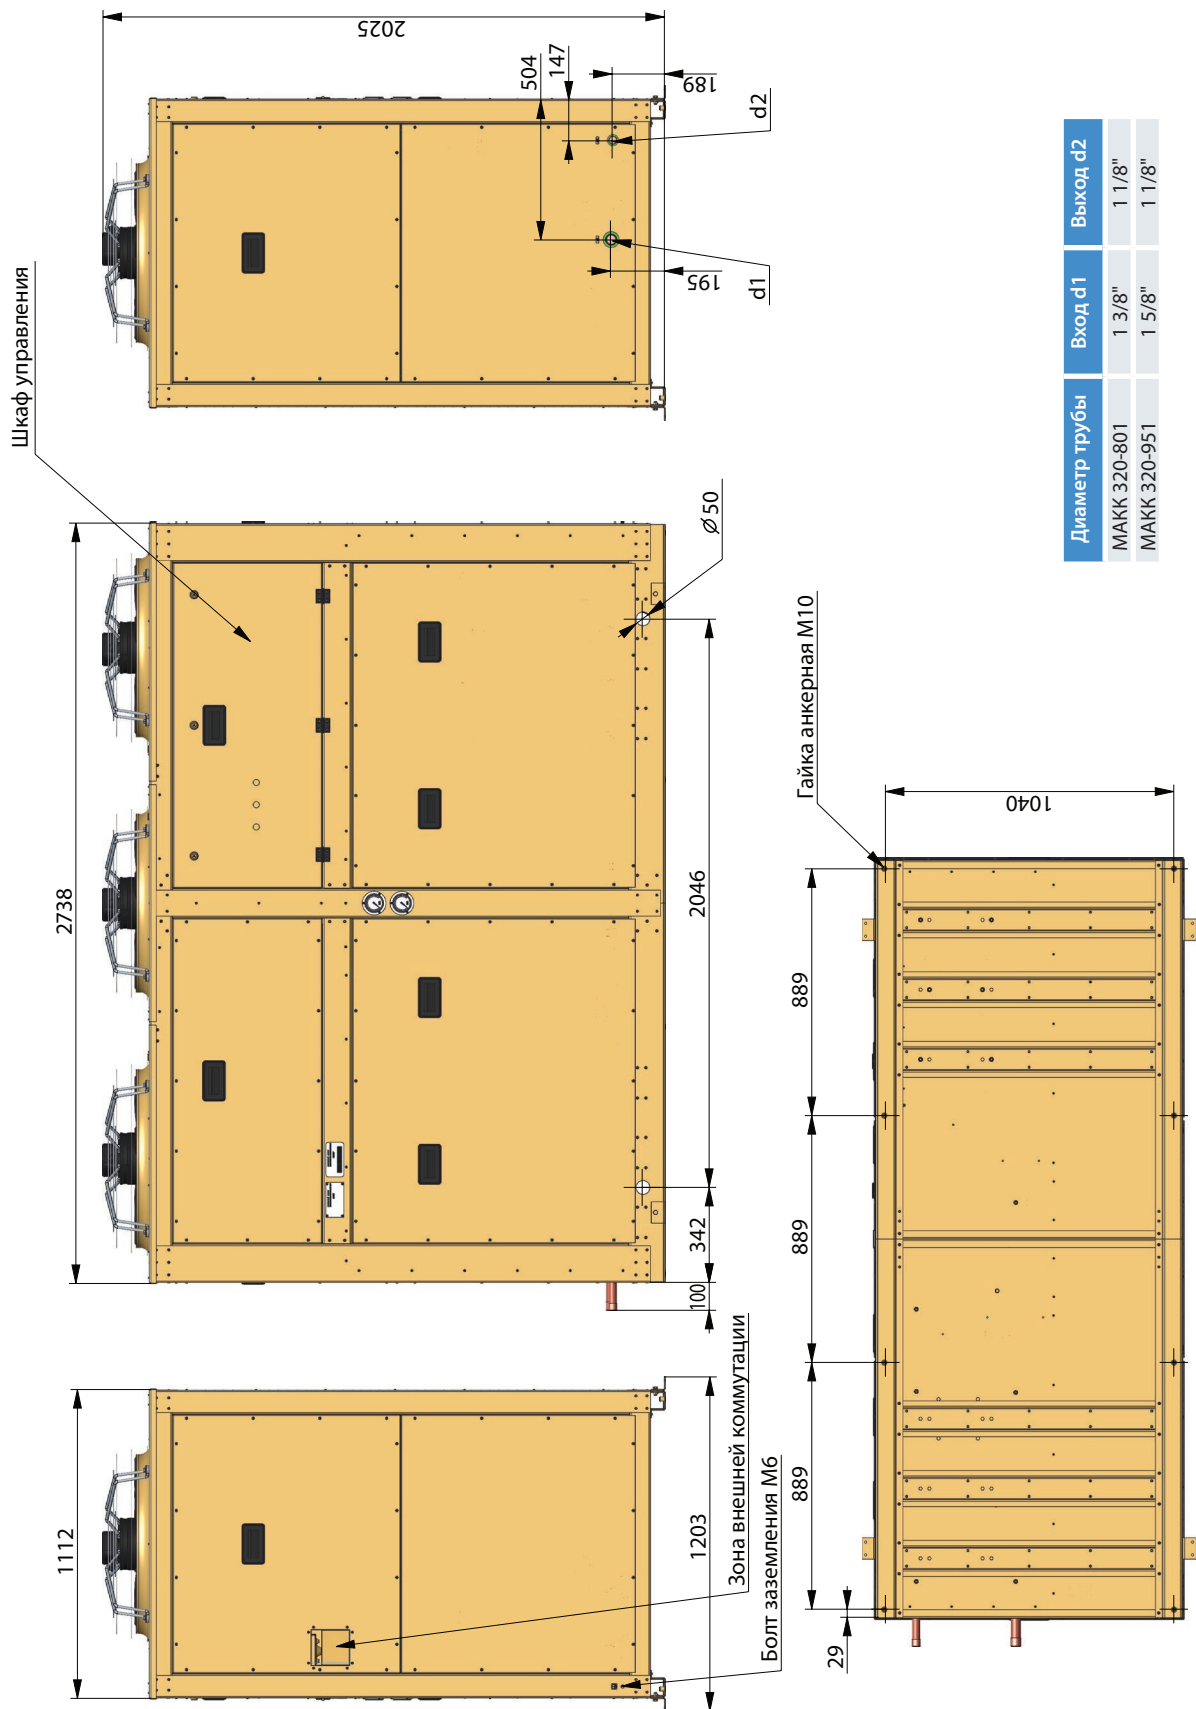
Агрегат компрессорный типа МАКК 320-801, -951
